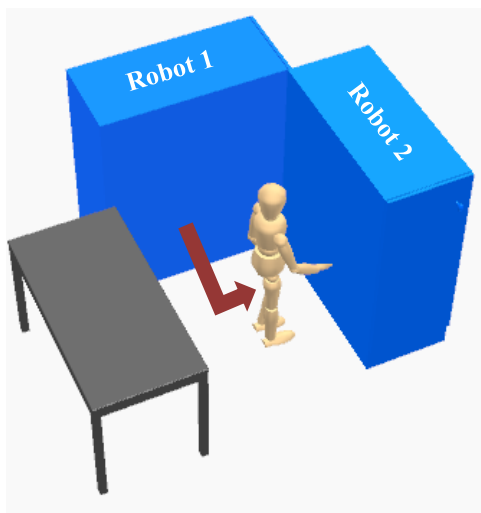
Entrada do *jig* no *robot 2* (soldadura das redes ao terminal) após a primeira soldadura.
